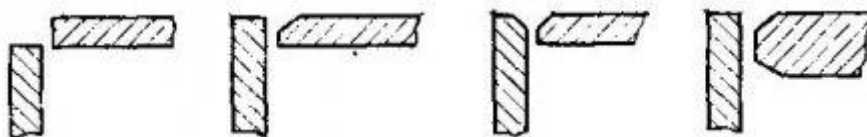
Форма подготовленных кромок под сварку для угловых соединений
